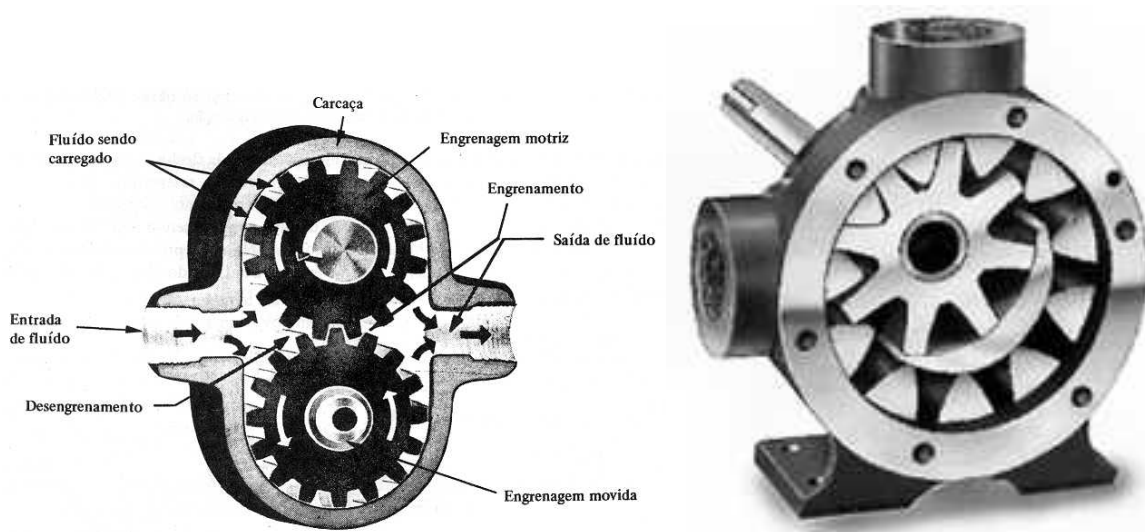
Bomba de engrenagens e bomba de engrenagens internas
